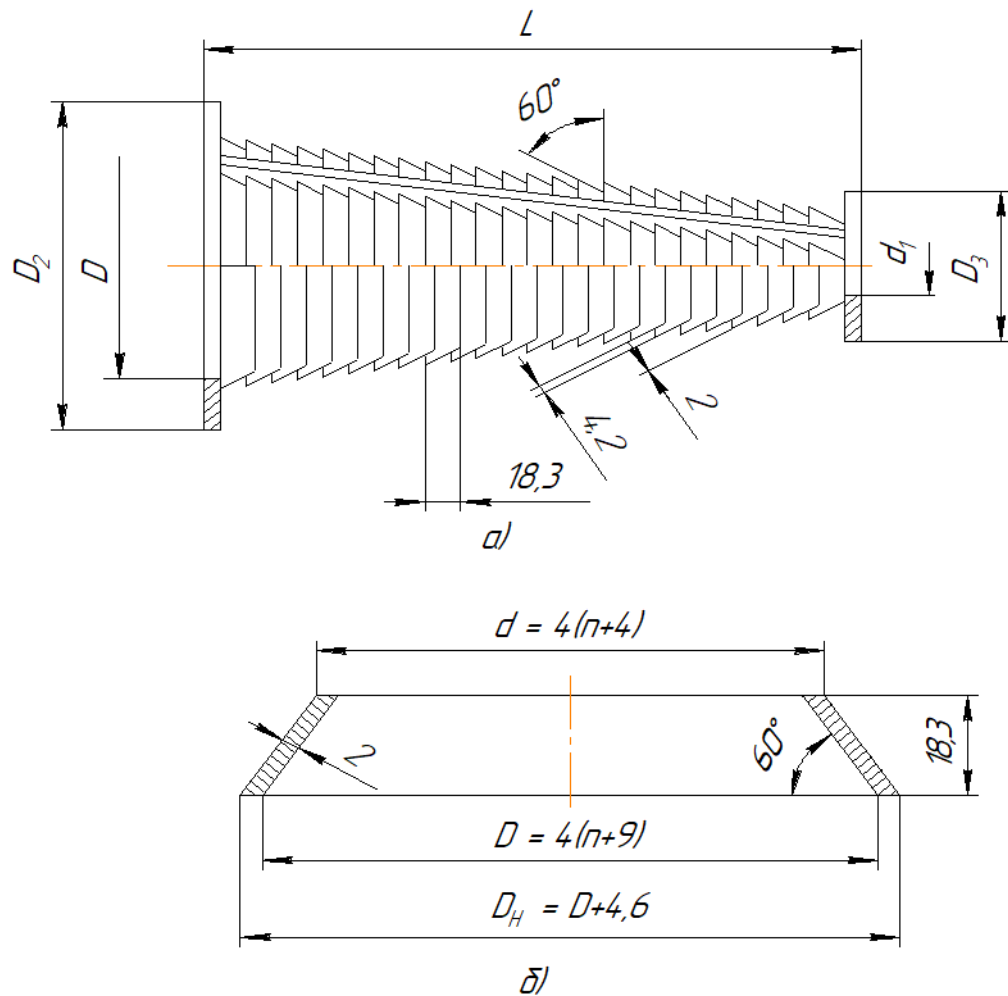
Розрахункова схема осадкового пристрою зерноочисного агрегату А1-БЛС-100
